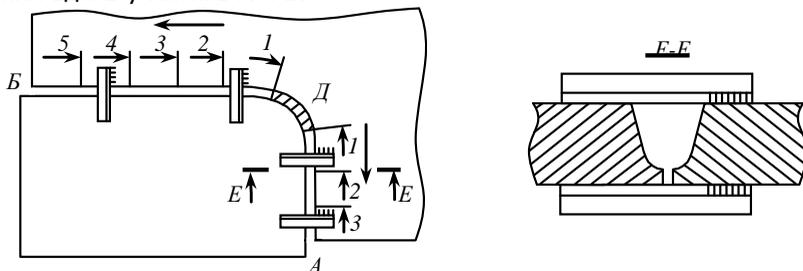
Сварка вставки с двумя свободными кромками без предварительного подогрева
